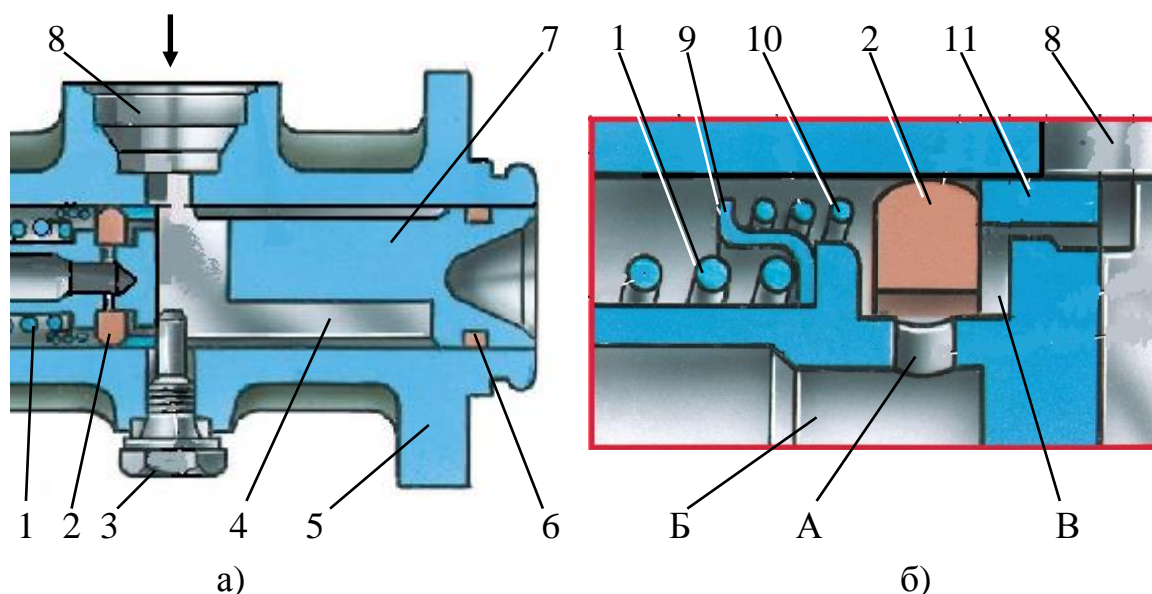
Обратный клапан главного тормозного цилиндра при отпущенной педали тормоза: 1 – возвратная пружина поршня; 2 – уплотнительное кольцо; 3 – упорный винт; 4 – паз поршня; 5 – корпус цилиндра; 6 – заднее уплотнение поршня; 7 – поршень; 8 – входное отверстие из дополнительного бачка; 9 – тарелка пружины; 10 – прижимная пружина уплотнительного кольца; 11 – распорное кольцо; А – радиальное отверстие в канавке поршня; Б – центральное отверстие поршня; В – зазор
